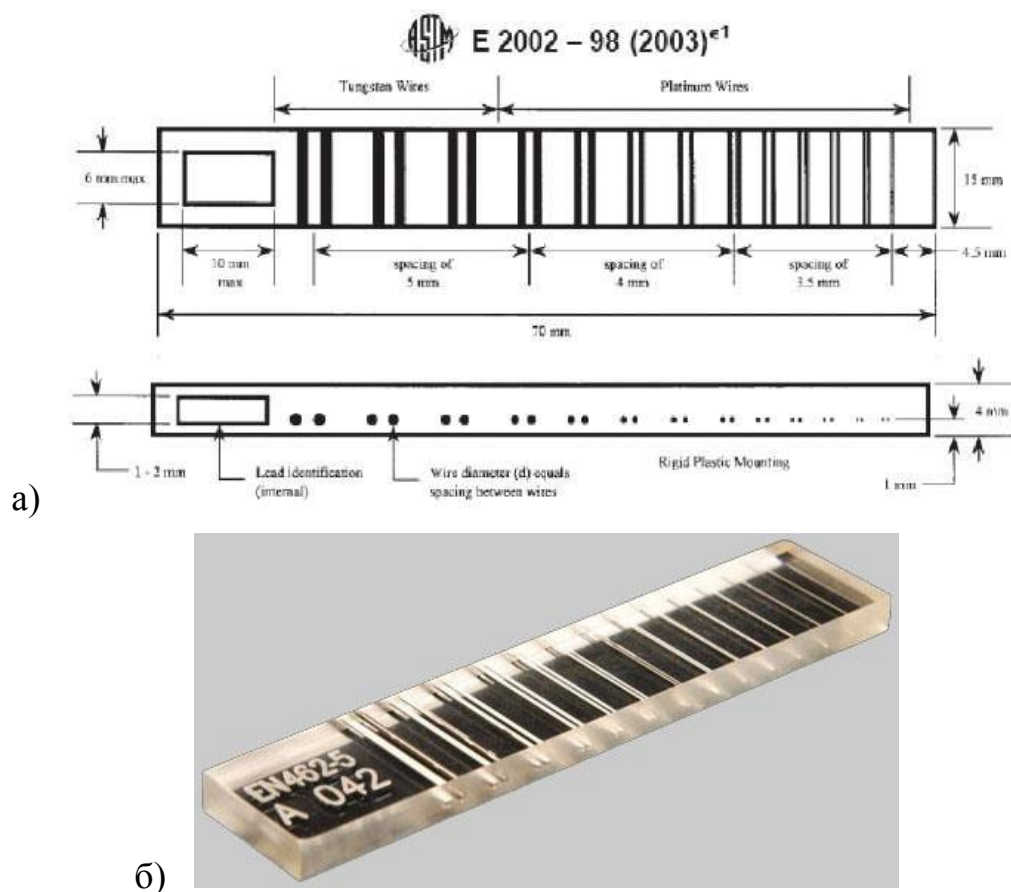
Чертеж индикатора (а) и его внешний вид (б)
